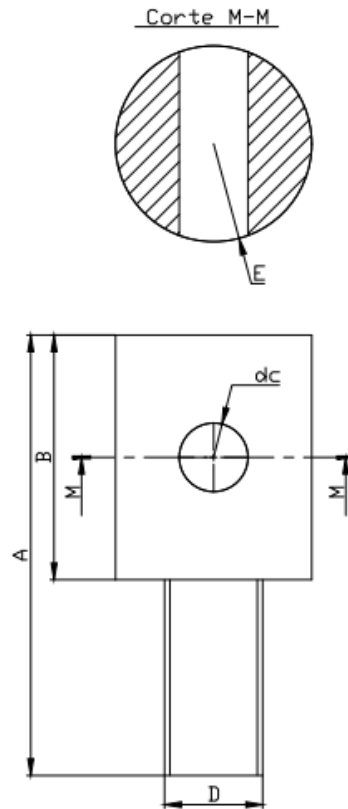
Esboço do apoio para Gancho de fixação (Fonte: Autor)
